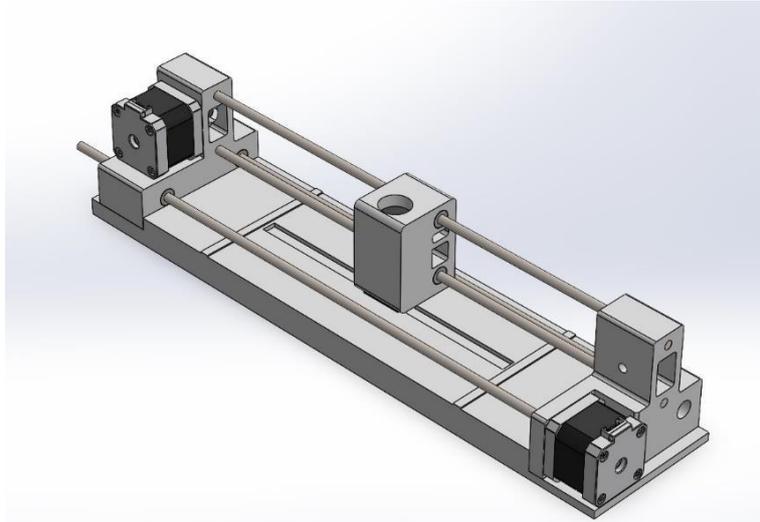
Diseño 3D impresora braille SolidWorks. Elaborado por el autor
